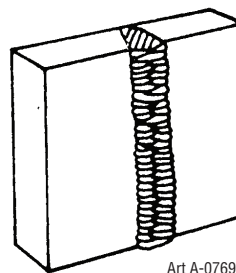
Position verticale, soudure bout à bout
